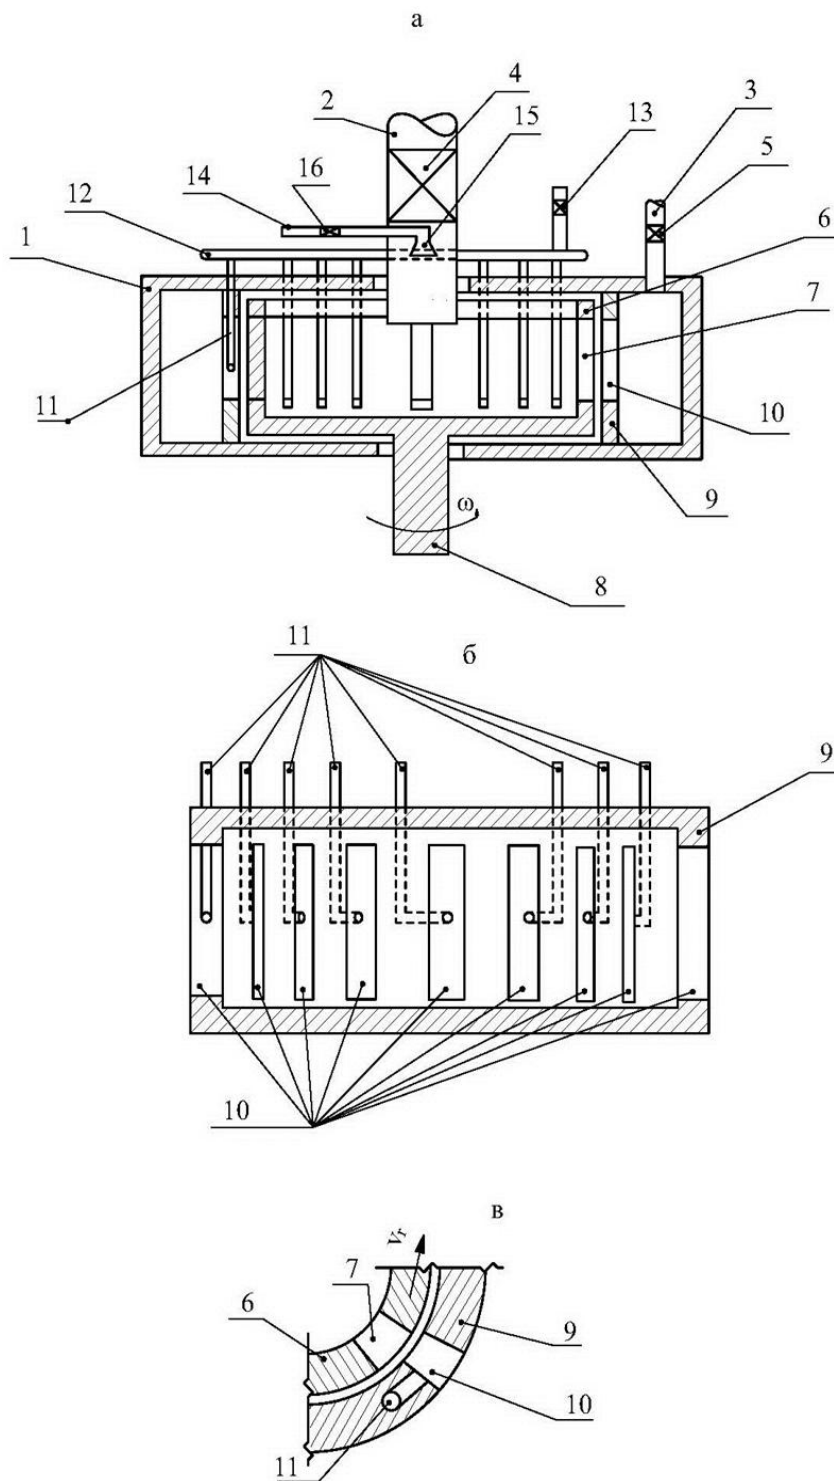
Роторный аппарат типа ДМП с регулируемым содержанием свободного газа в процессе приготовления рабочей жидкости для механизированных крепей: а – продольный осевой разрез диспергатора с модуляцией потока; б – статор с дополнительными каналами для подачи или отсоса газа; в – модулятор, образованный патрубками подвижного ротора и неподвижного статора
